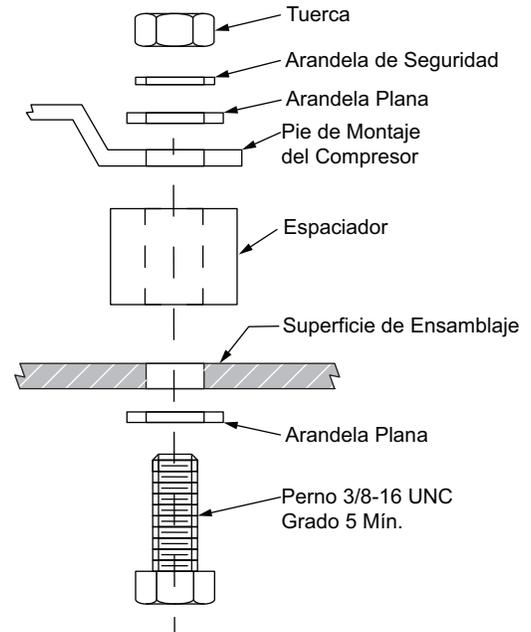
Montaje Rígido (Pie de Placa con Espaciador)
